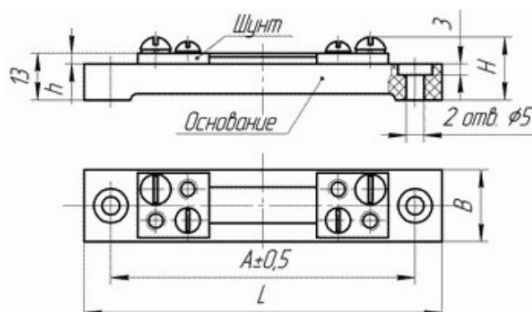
Габаритный чертеж шунта 75ШИП1-50-0.5
